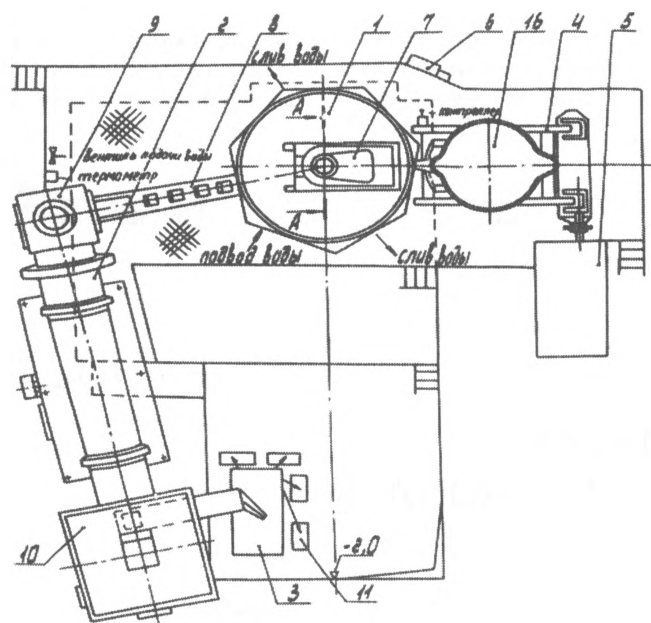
Схема дробелитейного комплекса мод. 4615К сталелитейного цеха №2 РУП "МАЗ": 1 – машина дробелитейная; 2 – барабан сушильный; 3 – виброгрохот; 4 – стенд для разливки стали; 5 – привод стенда для разливки стали; 6 – пульт управления дробелитейным комплексом; 7 – лоток; 8 – элеватор; 9 – бункер промежуточный; 10 – топка (сушило); 11 – контейнер для дробы; 12 – корпус; 13 – обечайка гранулятора; 14 – тарелка гранулятора; 15 – крыльчатка; 16 – ковш чайниковый; 17 – выпускное отверстие лотка; 18 – огнеупорный жидкостекольный состав №3; 19 – слой жидкого стекла; 20 – листовой асбест; 21 – слой кварцевого песка; 22 – кирпич огнеупорный шамотный ША-1 №6; 23 – кирпич огнеупорный шамотный ША-1-67, ША-1-96 и др.; 24 – подпятник гранулятора
